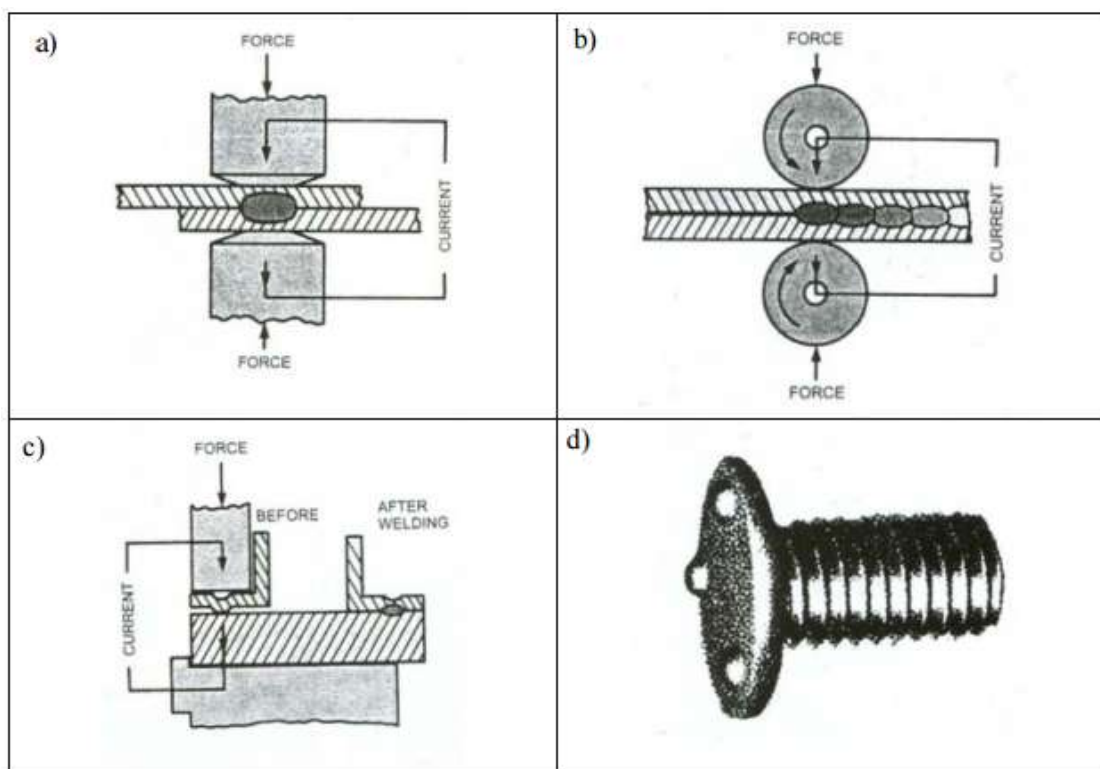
Procédés de soudage par résistance électrique, a) soudage par point, b) soudage à la molette, c) soudage par bossage, et d) soudage par bossage pour un goujon [2]
